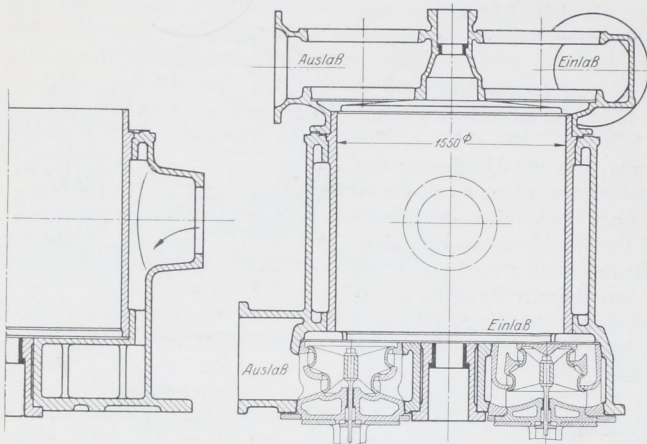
Zylinder mit Ventilsteuerung für stehende Maschinen.
